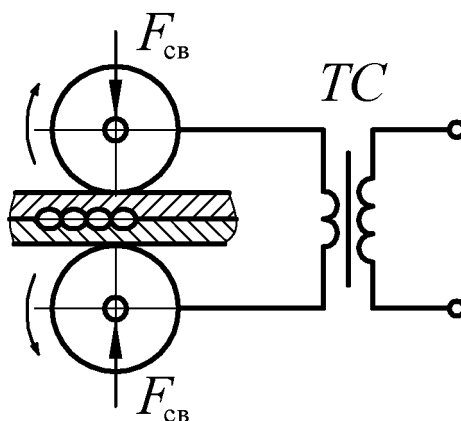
Схема процесса КШС ($ТС$ – сварочный трансформатор)
